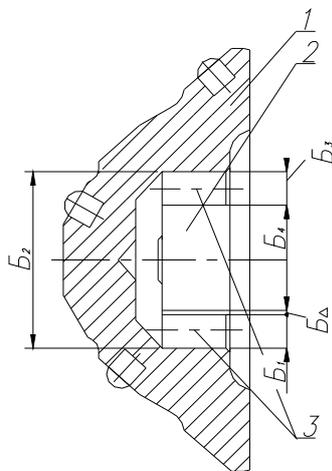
Схема установки шарошки: 1 - корпус шарошки; 2 - лапа; 3 - ролики
